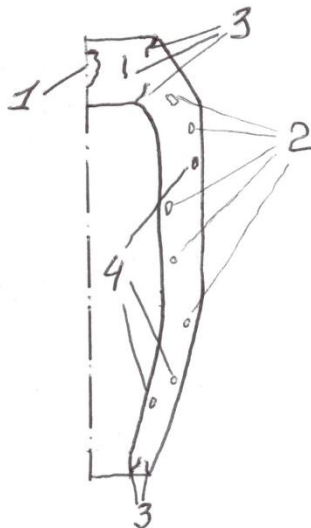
Распределение дефектов в заготовке корпуса снаряда (1 — усадочные раковины, 2 — газопористость, 3 — трещины, 4 — неметаллические включения)
